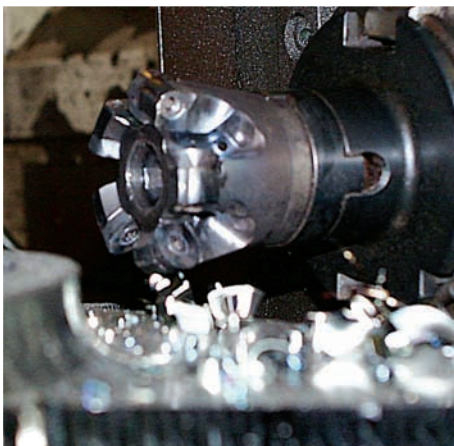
Der Schruppfräser R18 mit 47 mm \varnothing im Einsatz bei der Bearbeitung aus dem Vollen
